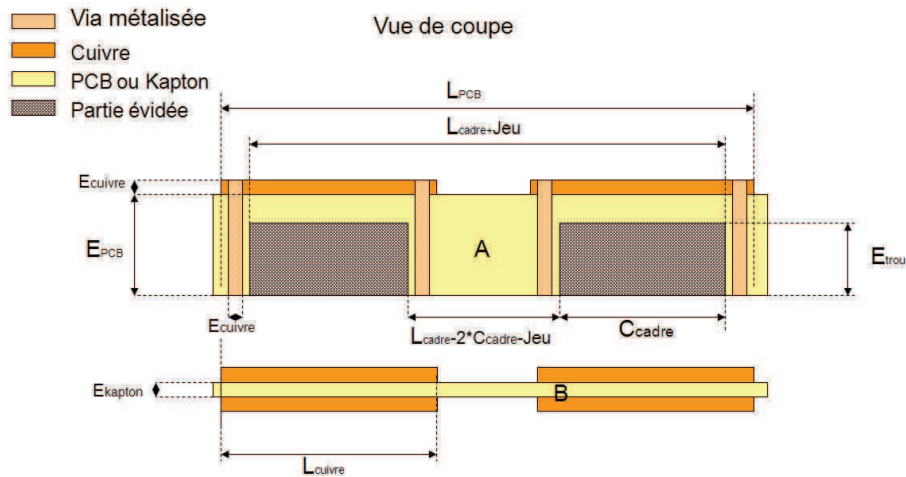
Vue de coupe schématique de l’inductance dans le PCB
